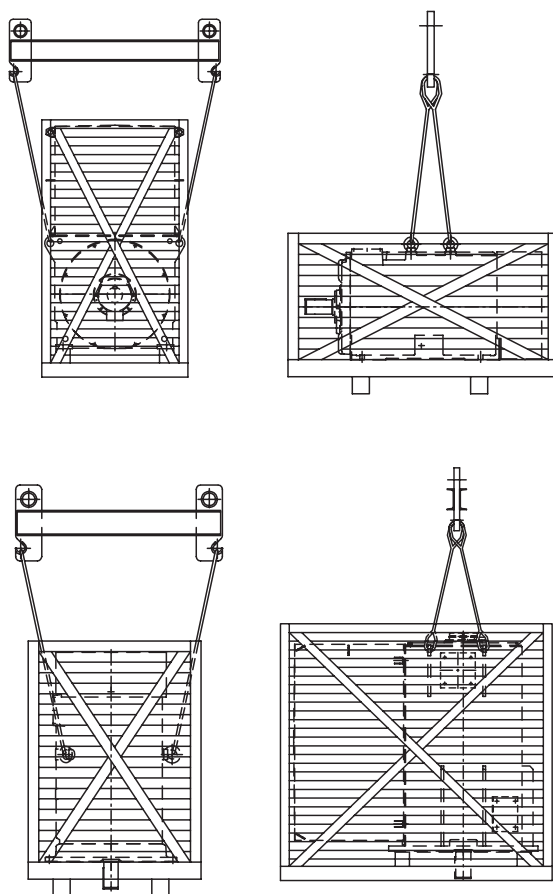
Elevación de máquinas verticales y horizontales en embalajes para el transporte marítimo
